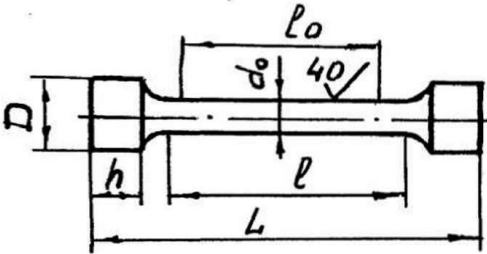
Форма зразків для випробування металу на статичний розтяг
